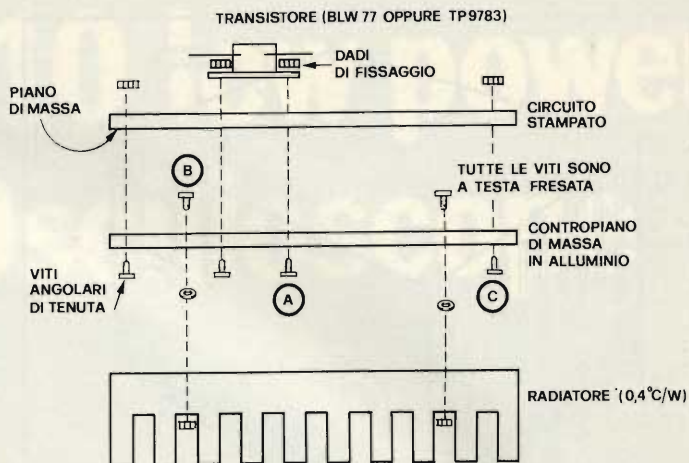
Assemblaggio meccanico dell'amplificatore.
